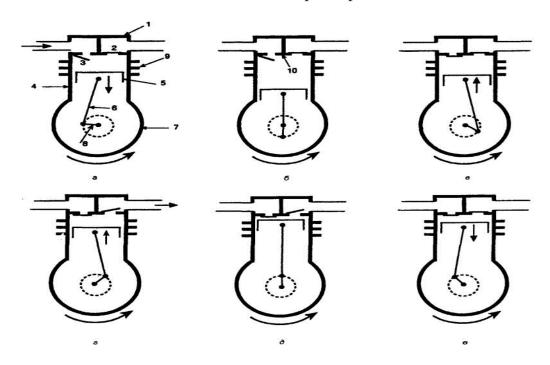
Принцип работы поршневого компрессора: 1 – головка блока; 2 – нагнетательный клапан; 3 – всасывающий клапан; 4 – блок цилиндров; 5 – поршень; 6 – шатун; 7 – картер; 8 – кривошип; 9 – охлаждающие ребра; 10 – клапанная плита
